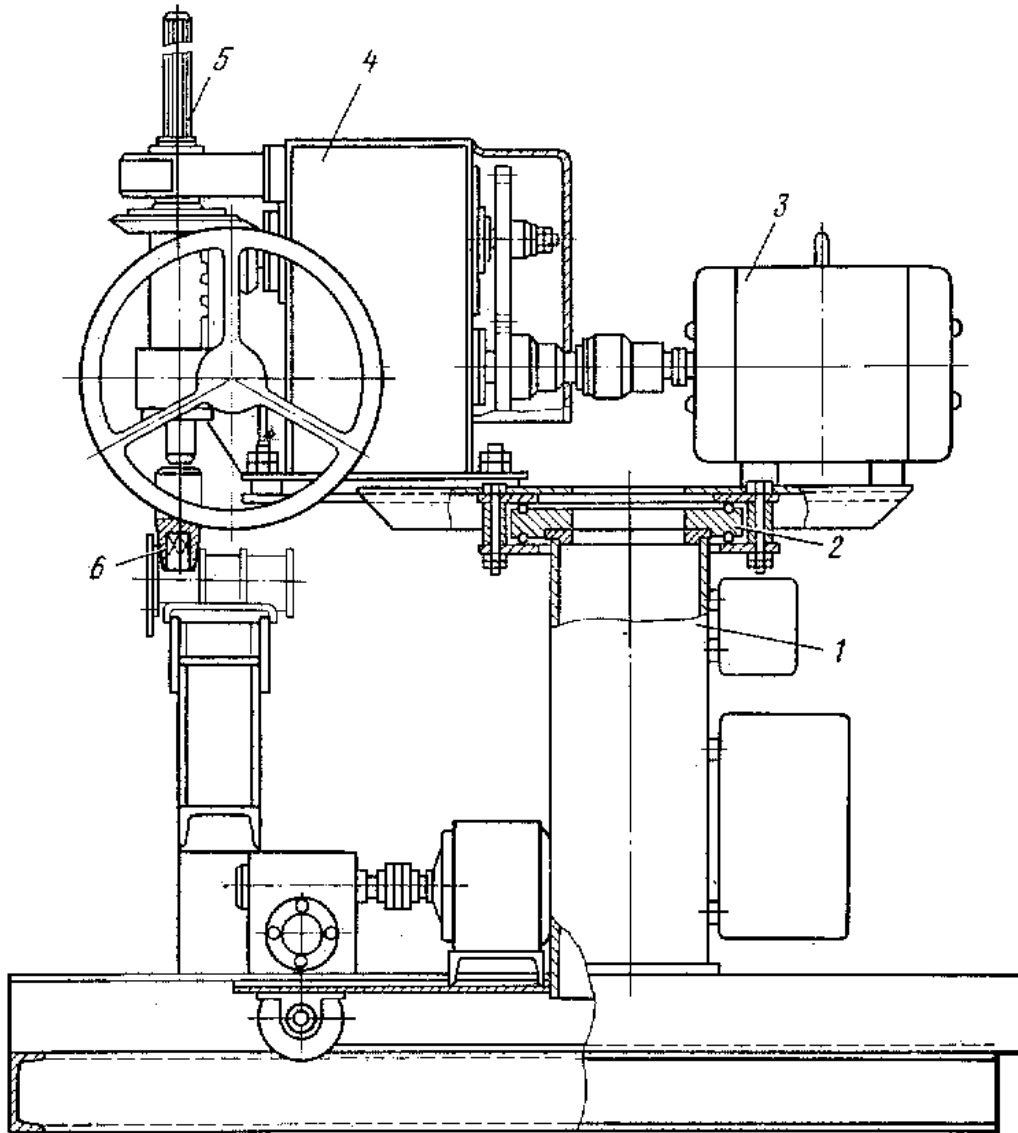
Електромеханічний стаціонарний гайковерт: 1 – колона, 2 – поворотна площадка, 3 – електродвигун, 4 – коробка переміни передач, 5 – шпиндель, 6 – змінні ключі
